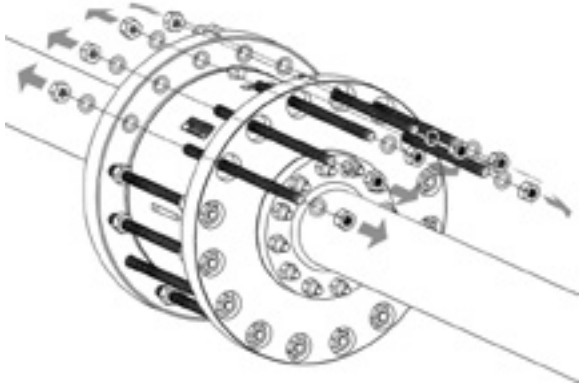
Entfernen Sie die oberen Bolzen und Muttern.
